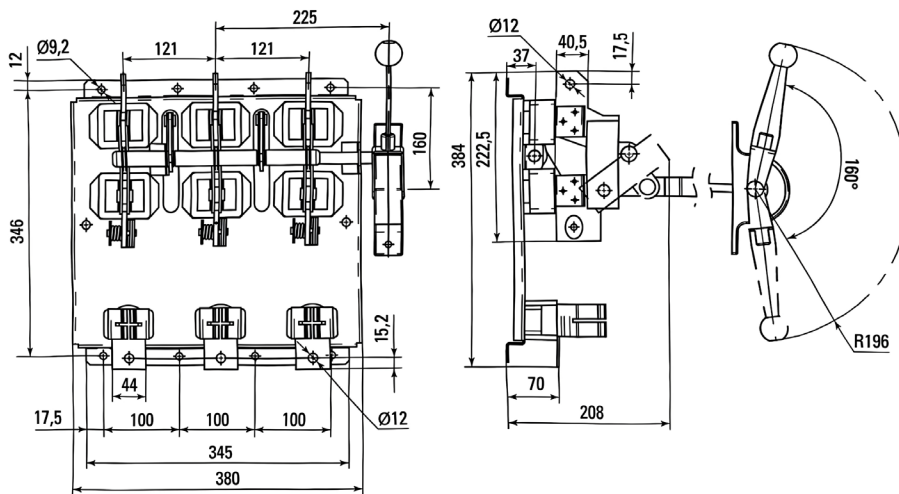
Размеры для установки привода передней смещенной рукоятки 630 А
